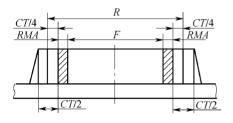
外对称加工表面或双侧加工 表面铸件基本尺寸示意图 R—铸件基本尺寸 F—零件尺寸 CT—铸件尺寸公差值
